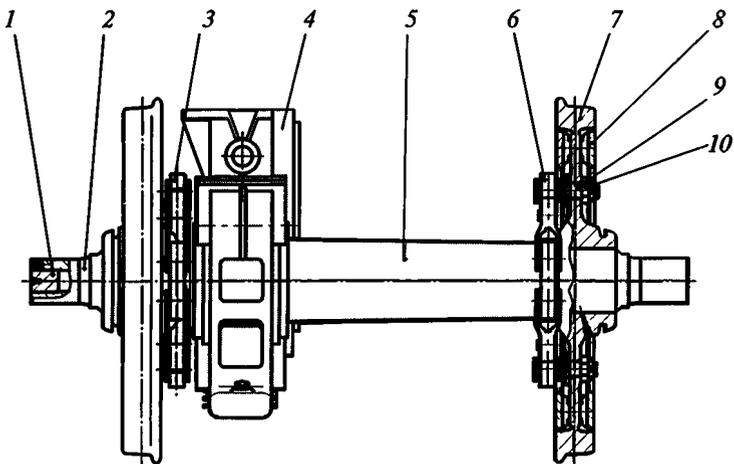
Колесная пара с редуктором и передаточным механизмом:
